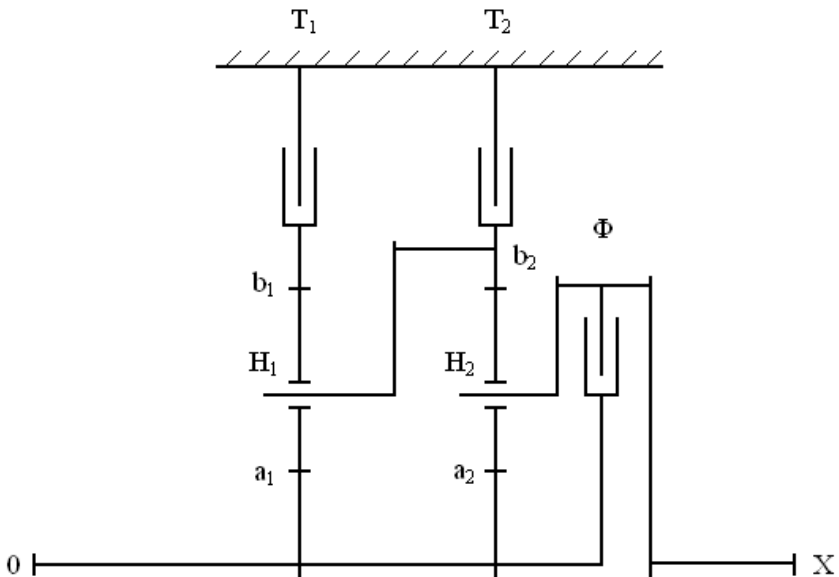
Схема трехступенчатого планетарного редуктора
